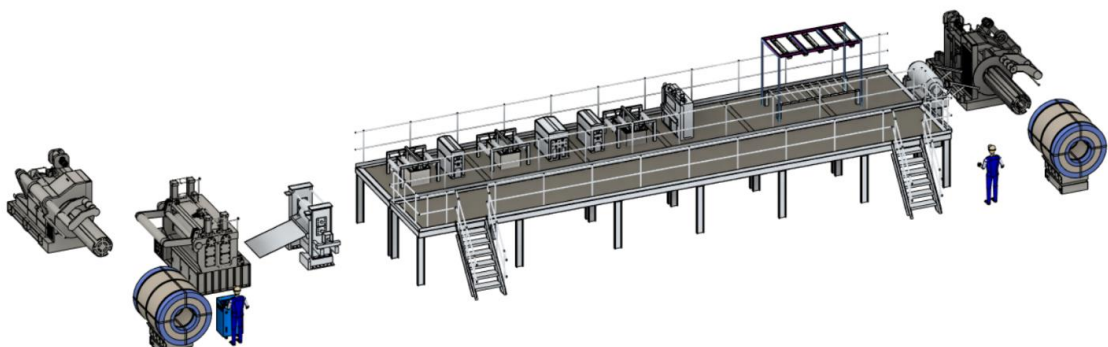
Bosquejo preliminar de la planta de cromado continuo.
